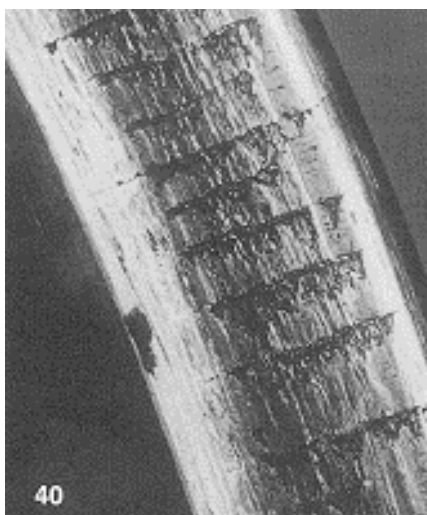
Задиры на поверхности торца внутреннего кольца цилиндрического роликоподшипника
